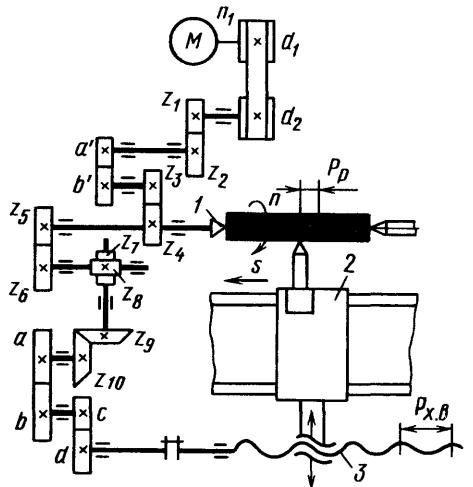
Упрощенная кинематическая схема нарезания резьбы на токарно-винторезном станке
